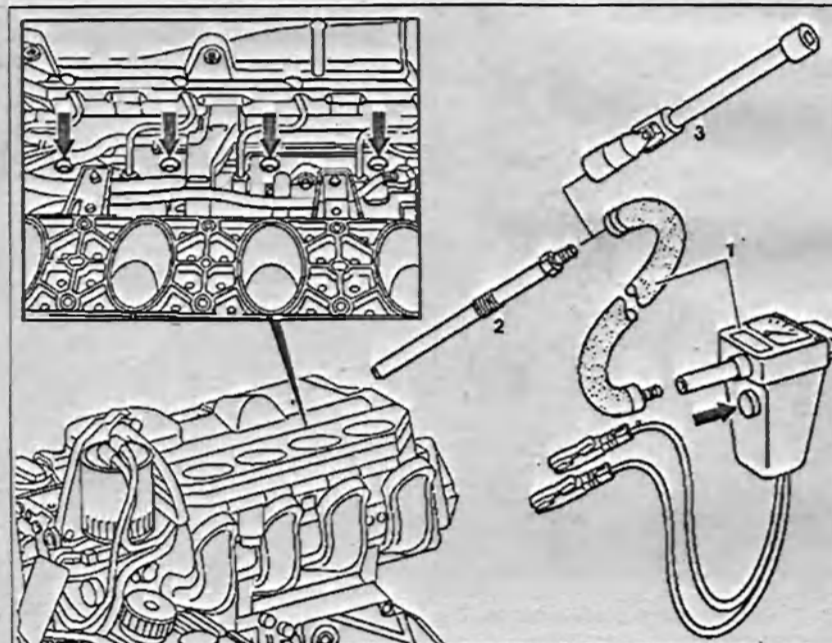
а. Проверка компрессии (на двигателях 611.981/983/987):
